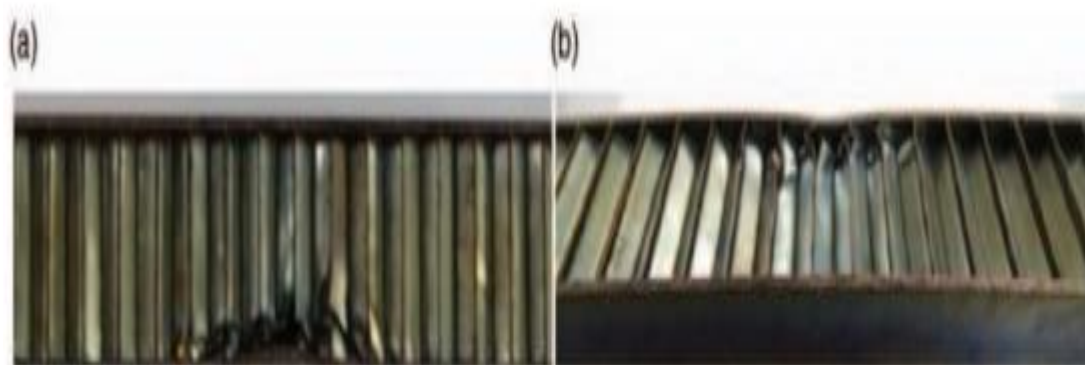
La section transversale d'un spécimen impacté à basse vitesse : (a) la vue de face ; (b) vue oblique.
